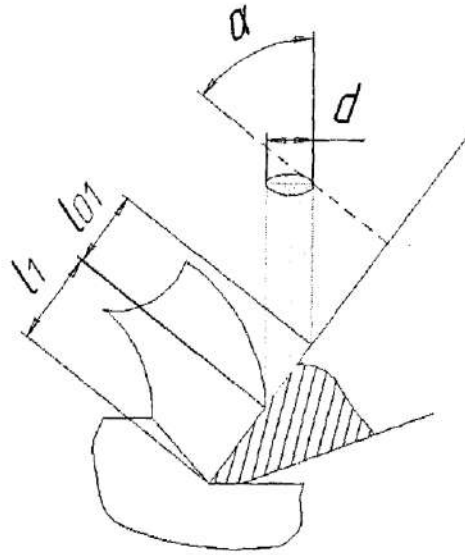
Схема охлаждения режущего инструмента при подаче СОТС на переднюю поверхность режущего клина.
